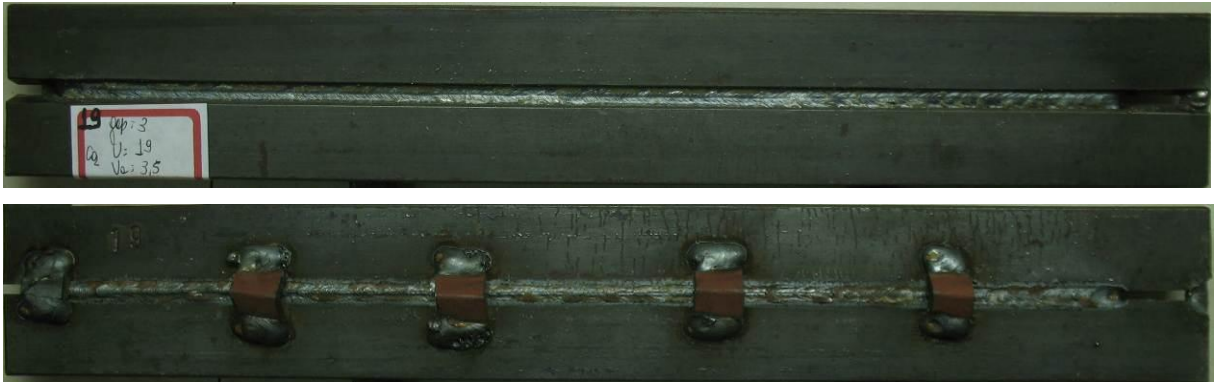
Teste 19 (face e raiz) (largura de cada chapa é 25 mm)
